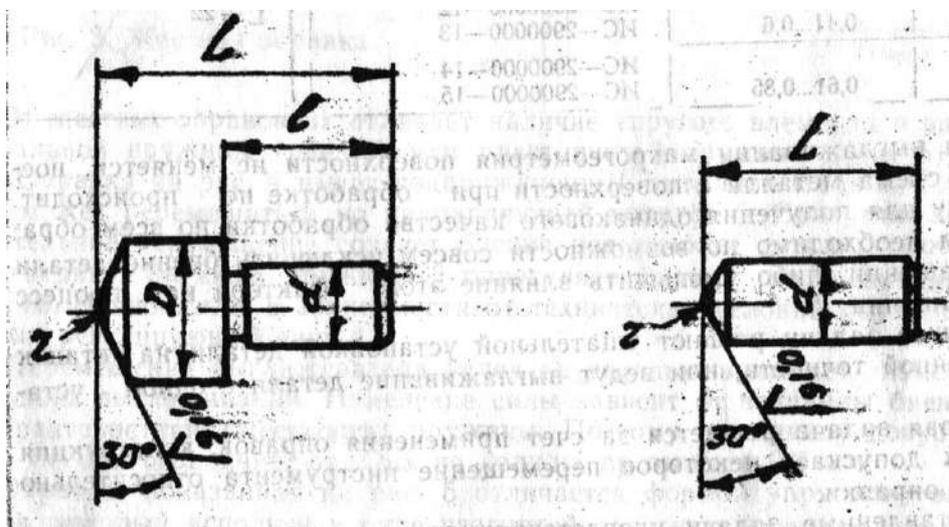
Типы выглаживателей со сферической рабочей поверхностью
